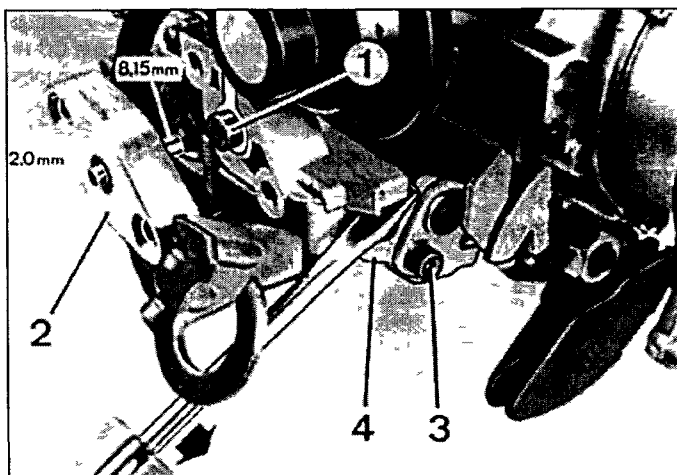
Установка пусковых оборотов - положение кулачка "прогрев"
